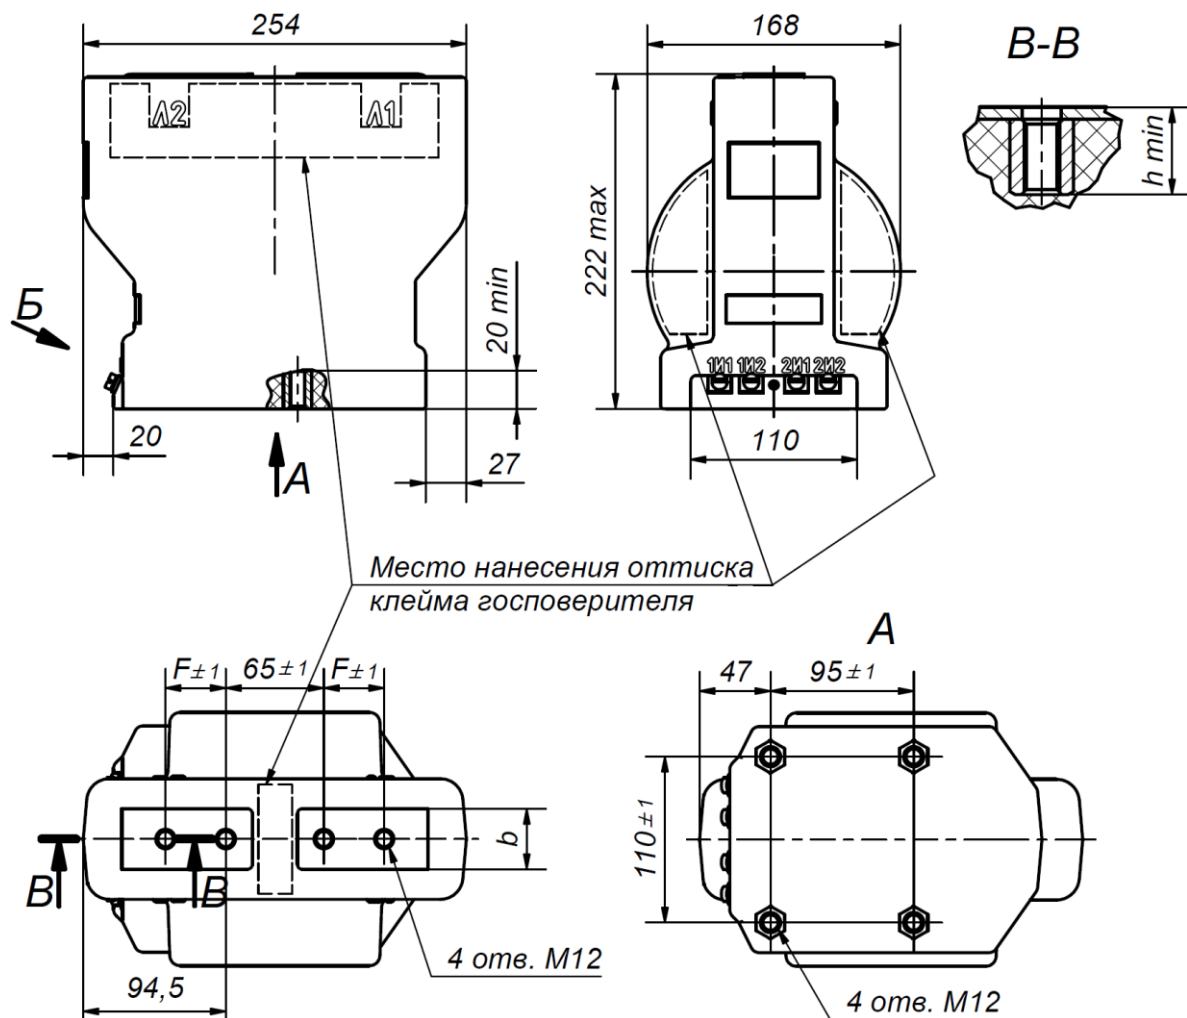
Габаритный чертёж трансформатора тока ТОЛУ-10-1.
